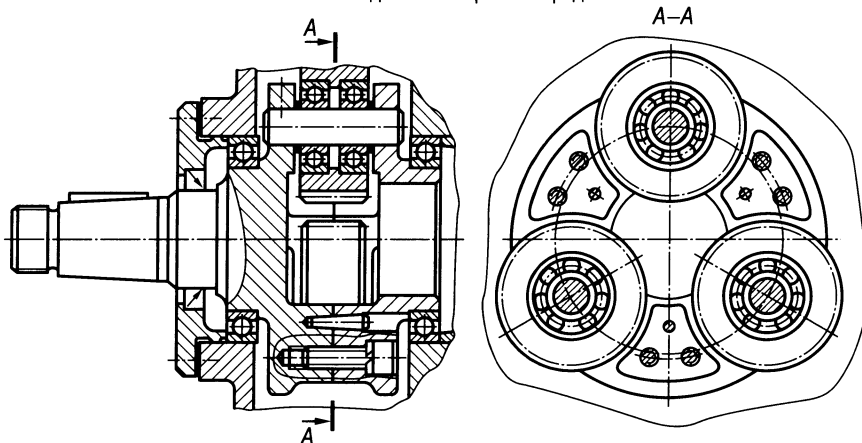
Разъемный вал-вилка планетарного зубчатого редуктора
